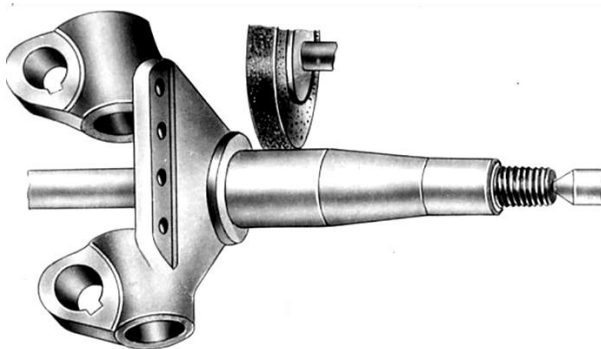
Схема шлифования под окончательный размер восстановленных поверхностей деталей
